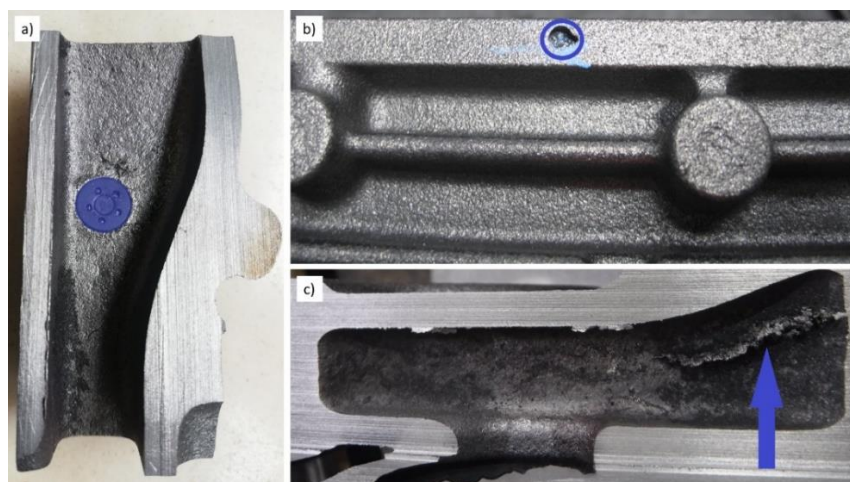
Defeitos dos blocos de motor 740: a) suporte do macho visível no interior da cavidade, b) bolha e c) penetração de metal em fissura do macho.
